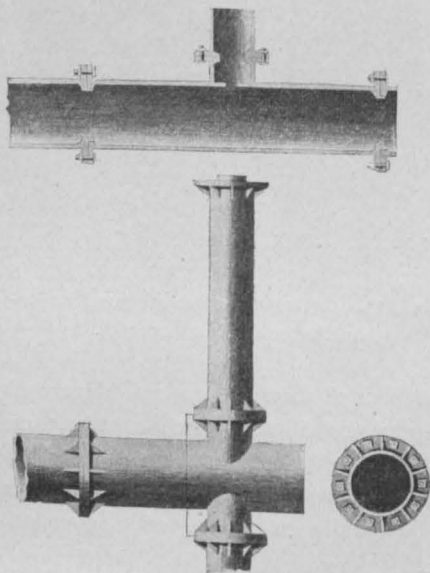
Rohrverbindungen nach REICHENBACH. 1811.
